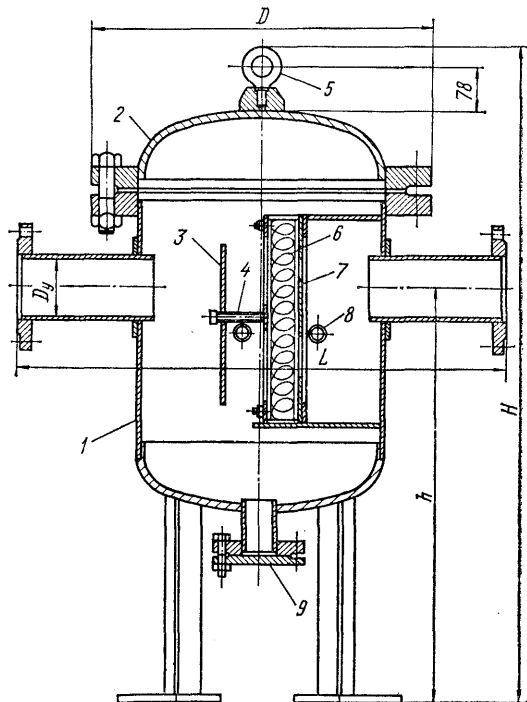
Фильтр кассетный сварной ФГ.
